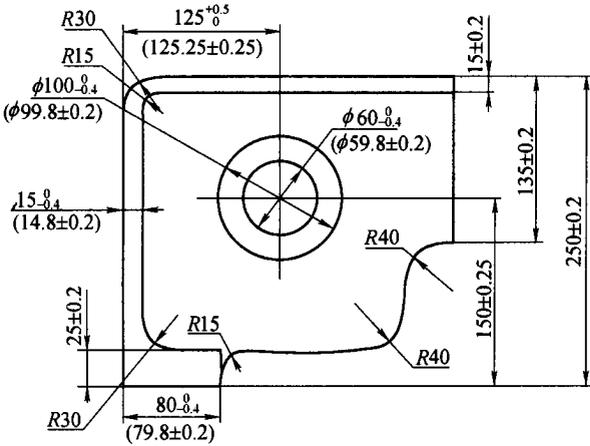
零件尺寸公差对编程尺寸的影响
